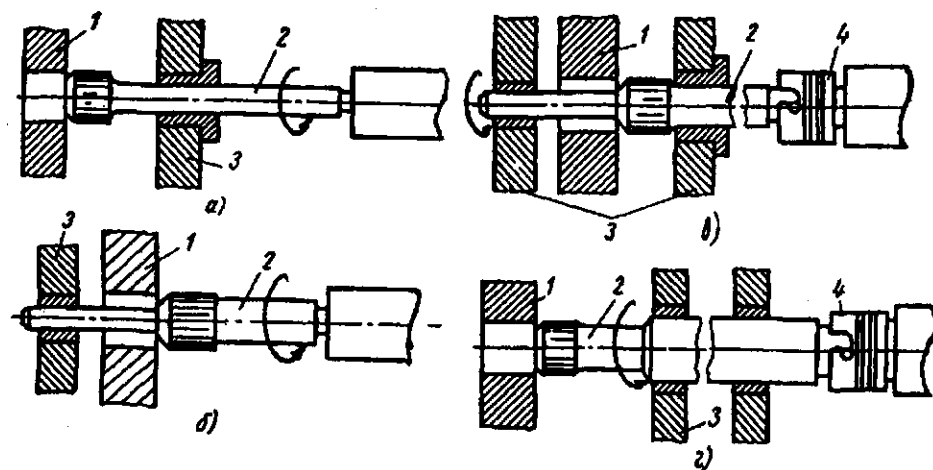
Схемы расположения направляющих устройств при растачивании корпусных деталей
